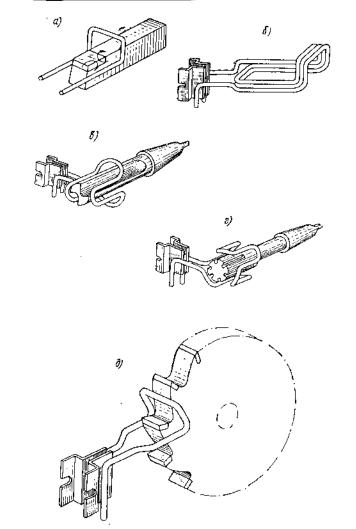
Индукторы для нагрева под пайку различного режущего инструмента:
